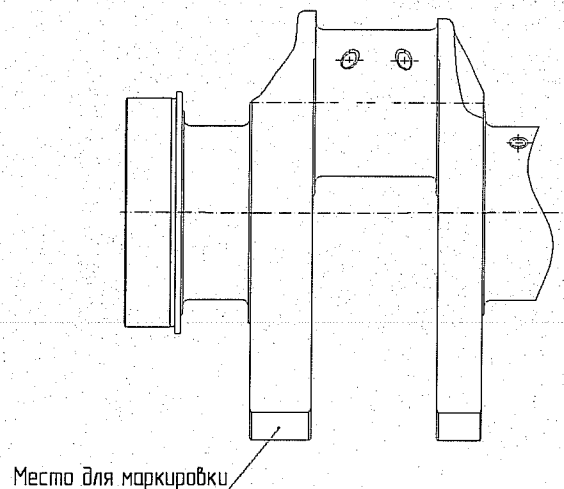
Место для маркировки варианта ремонтного размера шеек коленчатого вала
